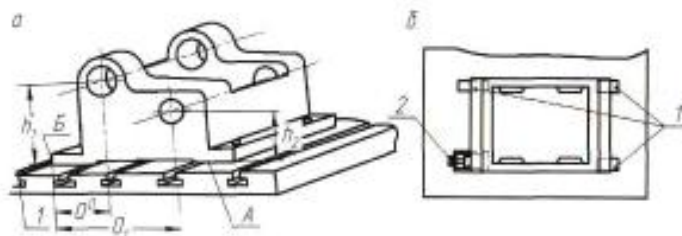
Установка заготовки с плоским основанием на стол станка: а – заготовка с точным плоским основанием; А – основание заготовки; Б – вспомогательная базовая поверхность; б – схема размещения подкладок и клинового домкрата при установке заготовки с неточным плоским основанием: 1 – подкладки; 2 – клиновой домкрат
